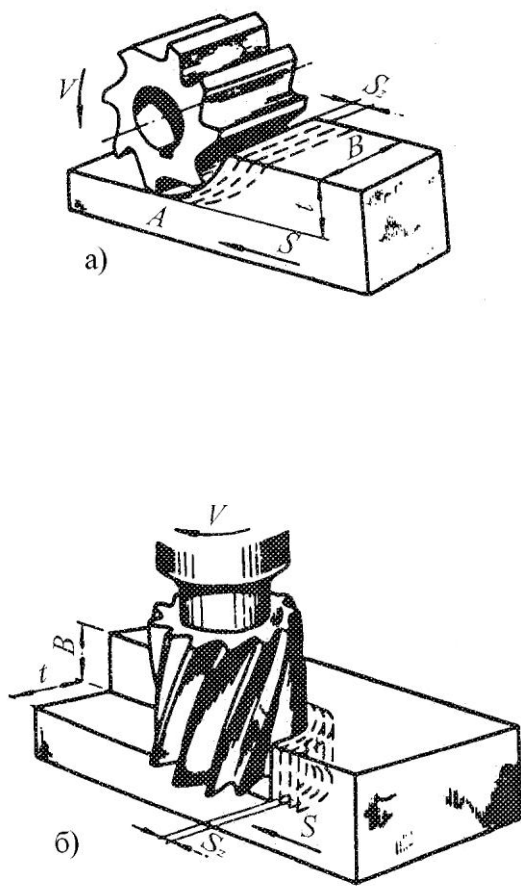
Фрезерування циліндричною (а) і кінцевою (б) фрезами
